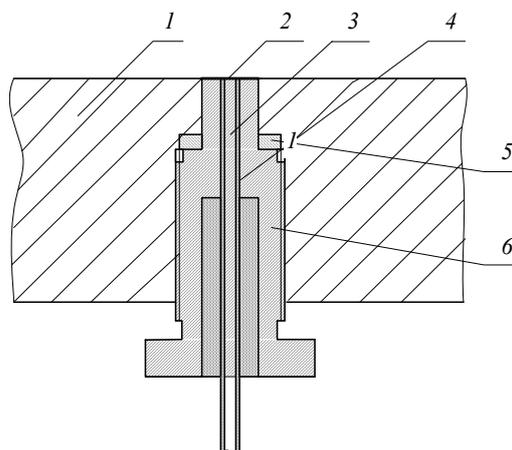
Схема установки и конструкция пленочной термопары: 1 – деталь; 2 – никелевая пленка; 3 – никелевый электрод; 4 – оксидная изоляция; 5 – уплотнительная шайба; 6 – корпус датчика
